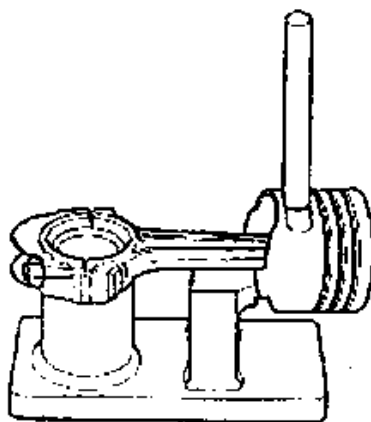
Montagem da ferramenta para a remoção do pino do êmbolo.
